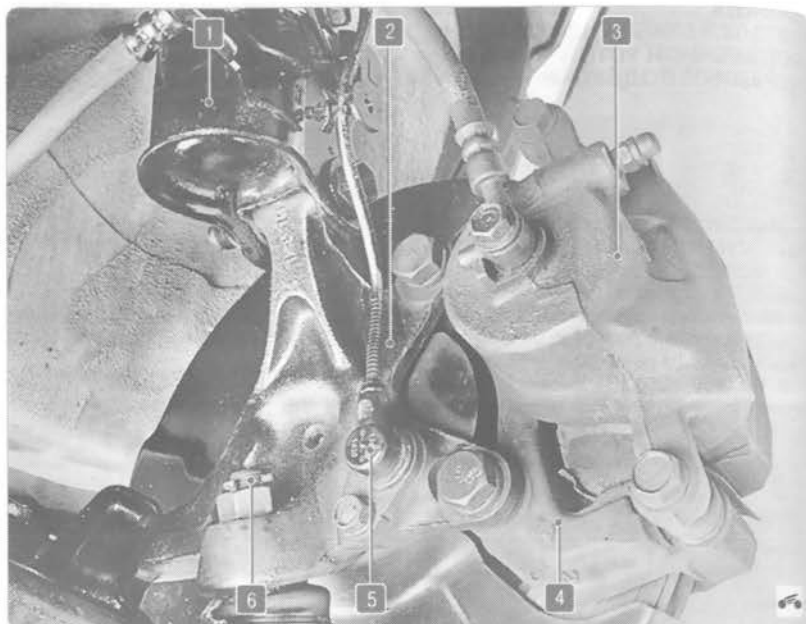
Поворотный кулак: 1 – амортизаторная стойка; 2 – поворотный кулак; 3 – суппорт; 4 – направляющая колодок; 5 – датчик скорости; 6 – палец шаровой опоры
